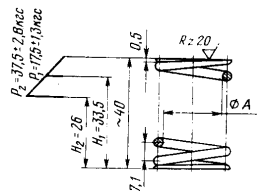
Упругость пружины клапана. Материал — проволока 51ХФА-А-П-ХН-3,5; твердость HRC 42... 50; A=20,4p<sup>3</sup>
